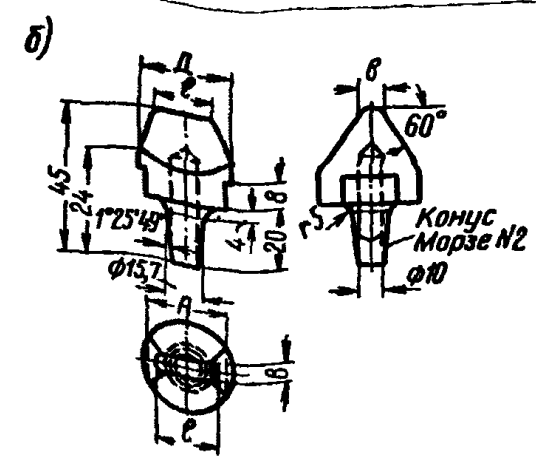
Электроды для сварки соединений стержней или профиля
